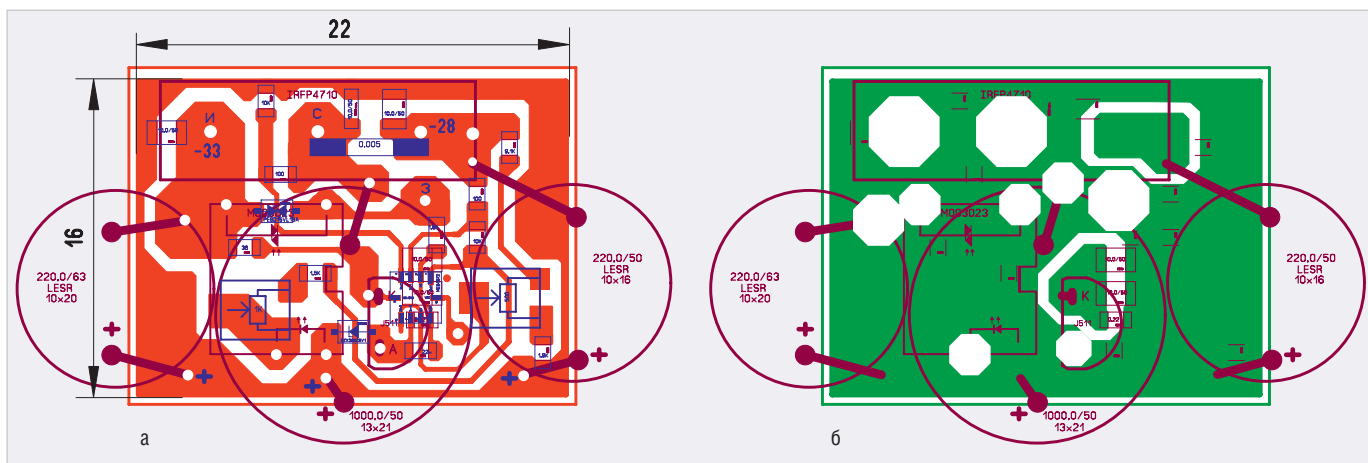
Разводка платы стабилизатора на микросхеме MC34072AMTБВГ (см. схему на рис. 2 [9]): а) вид со стороны дорожек; б) вид с обратной стороны (вид сквозь плату)
